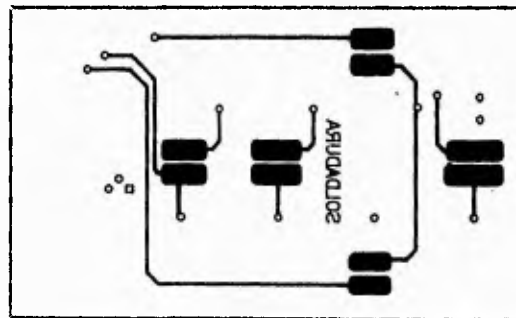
Cara de soldadura del circuito impreso del control remoto.
